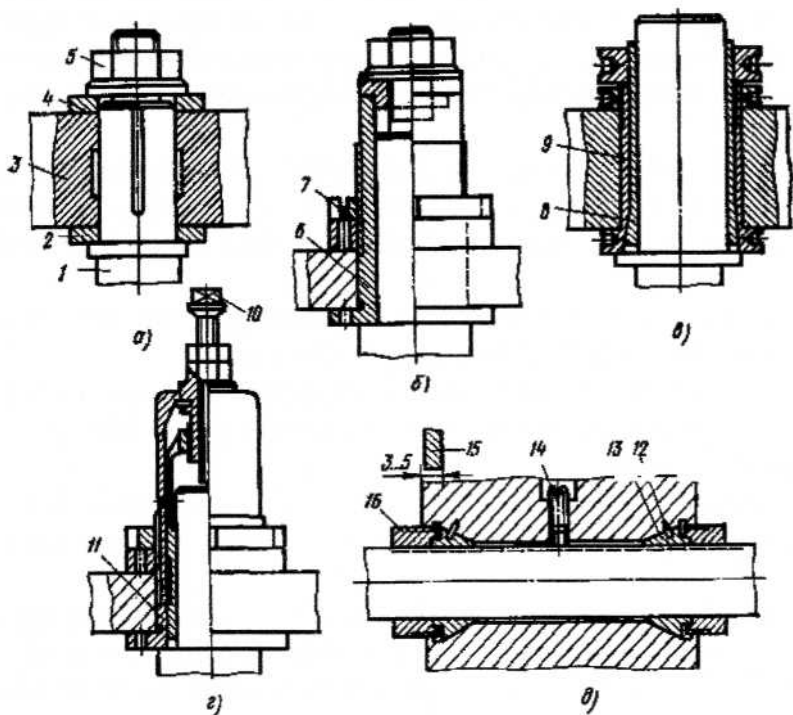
Способы крепления режущих инструментов в четырехсторонних продольно-фрезерных станках:
